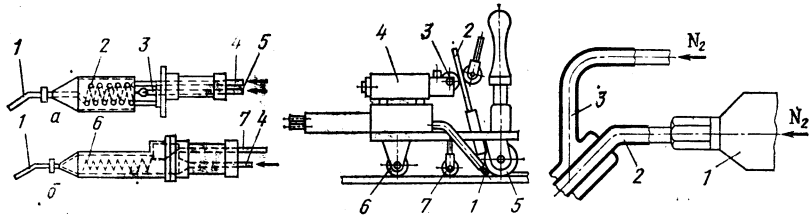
Ручной аппарат для сварки нагретым газом: а — нагреваемый газом аппарат для сварки нагретым газом; б — аппарат для сварки нагретым газом с электронагревом; 1 — сменное сварочное сопло; 2 — змеевик для нагретого газа; 3 — сменное сопло для горючего газа; 4 — газопровод газа для сварки; 5 — газопровод горючего газа; 6 — сменный электронагревательный элемент; 7 — к источнику питания
